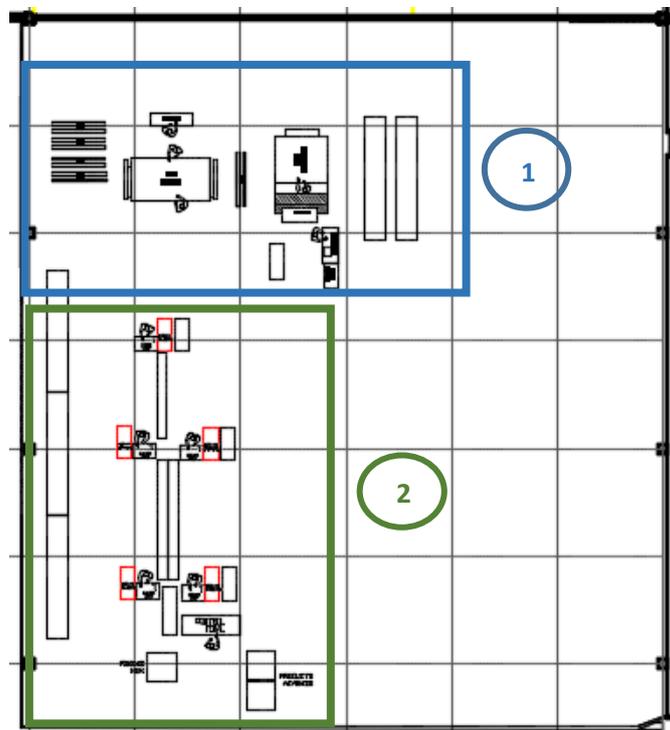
Layout inicial de las estaciones de trabajo (Zona 1 en color azul: Revisión de piel, Marcado, Troquelado y Rebajado; Zona 2 en color verde: Almacenamiento, Cosido y Control final y embalaje). Fuente: Elaboración propia
